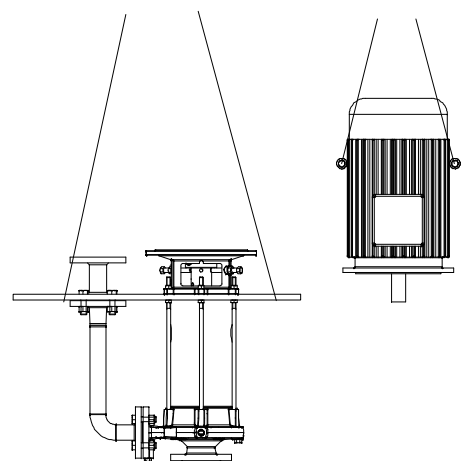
Транспортировка насоса / двигателя типоразмеров, начиная с 180
